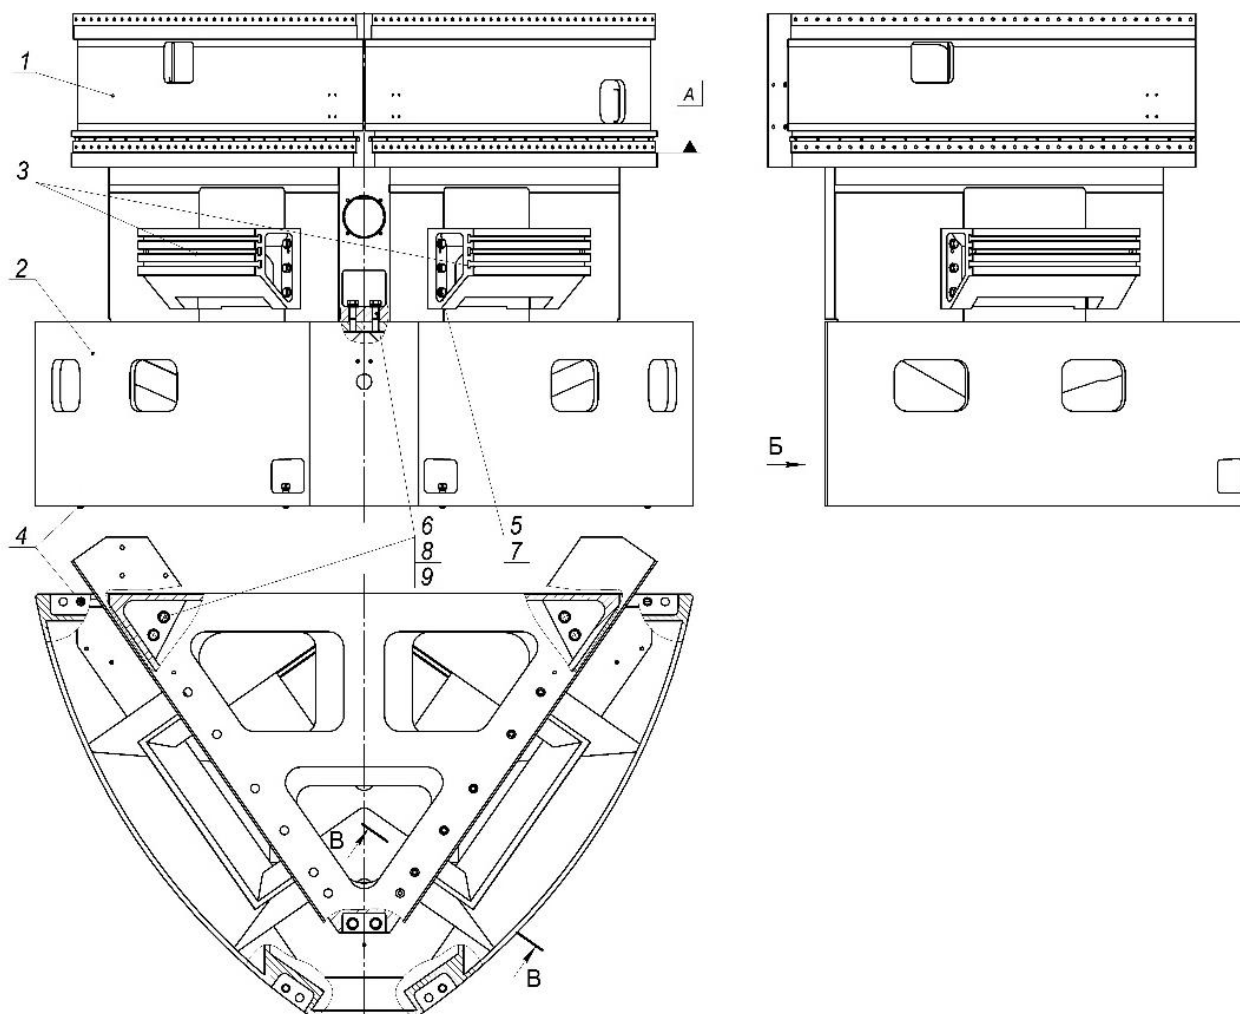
Станина вертикального двошпindelного токарного верстата з ЧПК мод.ПАБ-350
